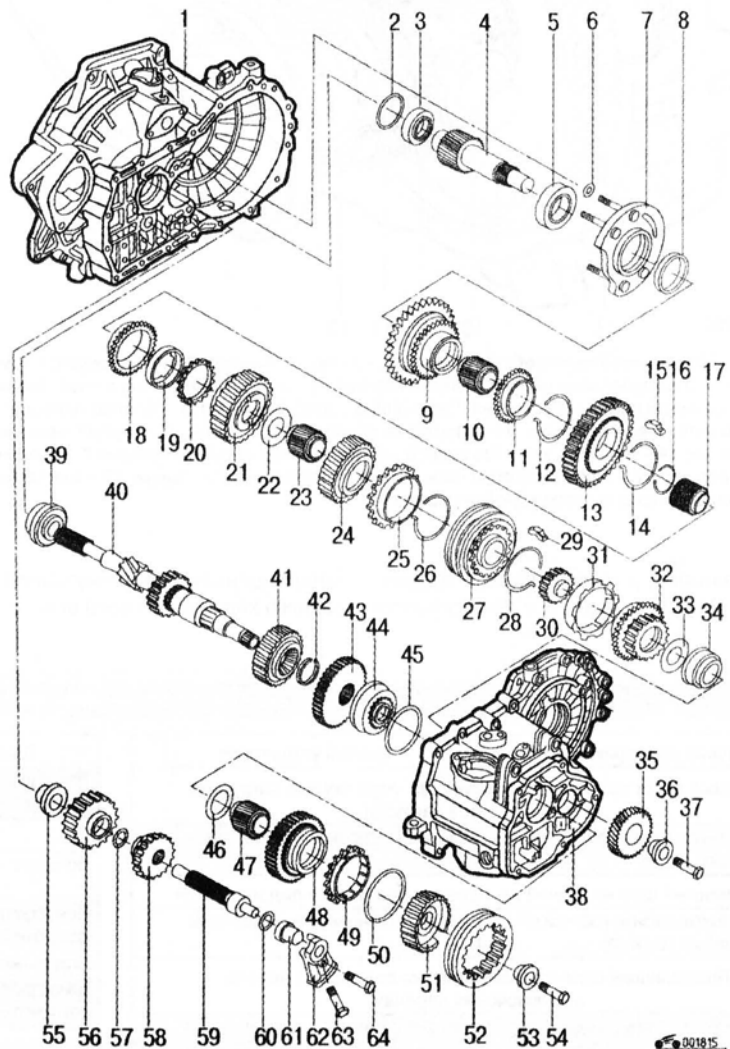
Вали и шестерни пятиступенчатой коробки передач: 1 – картер сцепления; 2 – регулировочная шайба; 3 – конический подшипник (малый); 4 – вторичный вал; 5 – конический подшипник (большой); 6 – шайба круглого сечения; 7 – опора подшипника; 8, 22, 33, 46, 60 – упорные шайбы; 9 – шестерня I передачи; 10, 23, 30, 47 – игольчатые подшипники; 11, 18, 25, 31, 49 – кольца синхронизаторов; 12, 14, 26, 28 – пружины; 13, 15, 29, 27 – синхронизаторы; 16, 17 – стопорные кольца игольчатого подшипника; 19 – внешнее кольцо синхронизатора; 20 – внутреннее кольцо синхронизатора; 21 – шестерня II передачи; 24 – шестерня III передачи; 32 – шестерня IV передачи; 34, 36, 53, 55, 61 – втулки; 35 – шестерня V передачи; 37, 54 – болты М8х26; 38 – картер коробки передач; 39 – роликовый подшипник; 40 – первичный вал; 41 – шестерня I передачи; 42 – стопорное кольцо; 43 – шестерня IV передачи; 44 – роликовый подшипник; 45 – регулировочное кольцо; 48 – шестерня V передачи; 50 – пружина; 51 – ступица синхронизатора; 52 – скользящая муфта синхронизатора; 56 – промежуточная шестерня; 57 – стопорное кольцо; 58 – шестерня передачи заднего хода; 59 – вал шестерни передачи заднего хода; 62 – держатель вала заднего хода; 63 – винт продольного крепления держателя; 64 – винт поперечного крепления держателя
